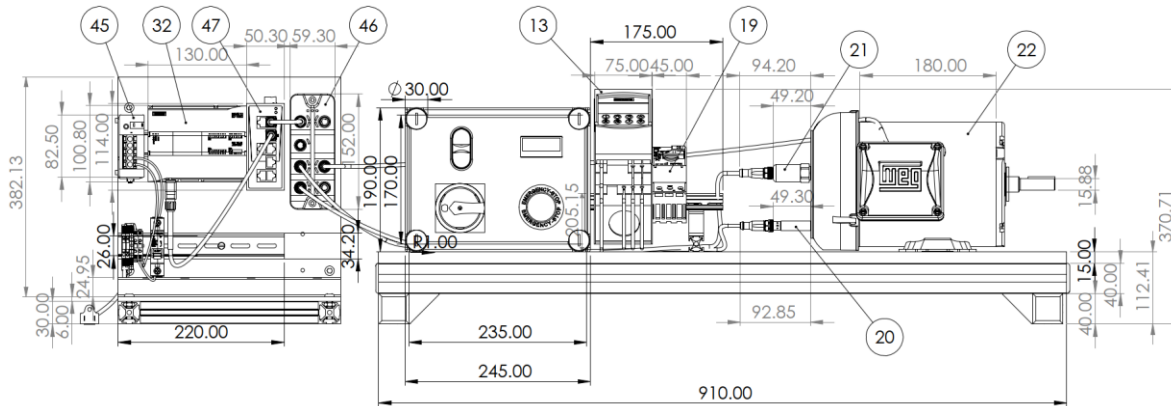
Vistas de dibujo técnico (dimensiones) del banco de pruebas.
